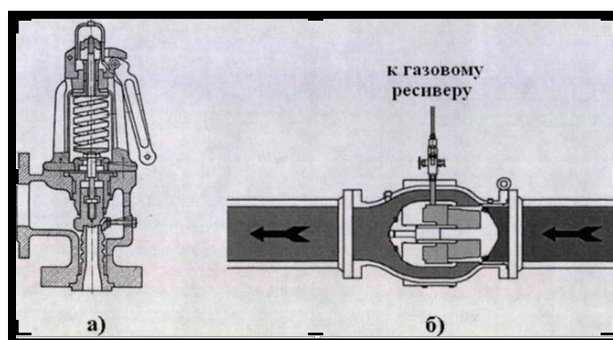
Предохранительный клапан с газовым ресивером:
